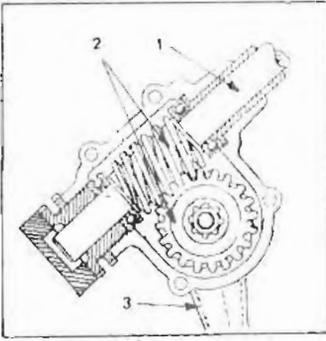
Caja de dirección. 1.- Columna de dirección. 2.- Engranaje sinfín. 3.- Brazo.
